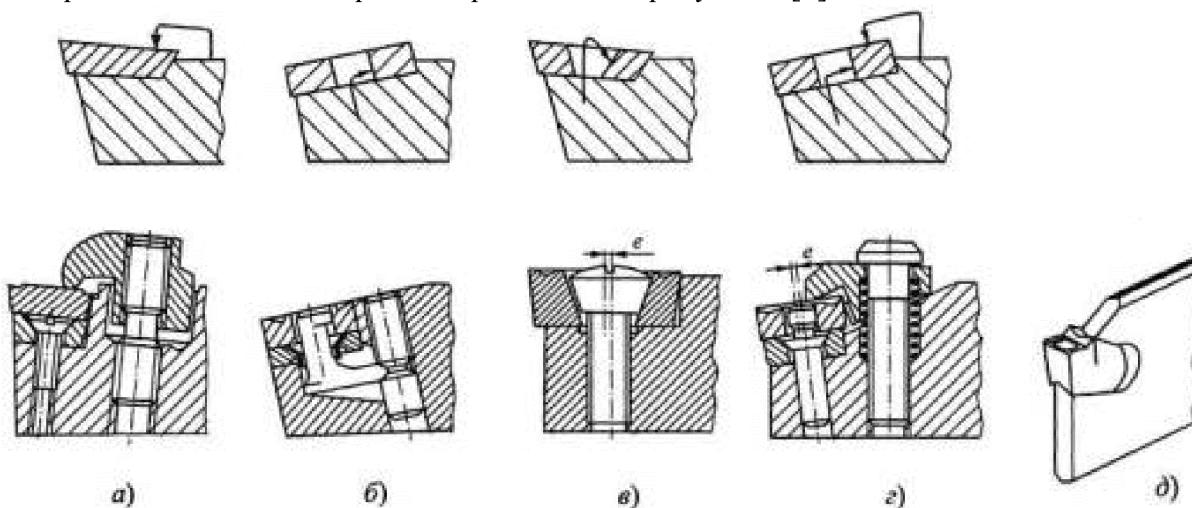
схемы механического крепления режущих пластин: а – прихватом сверху; б – рычагом через отверстие; в – винтом с конической головкой; г – штифтом через отверстие и прихватом сверху; д – за счет упругой деформации стенки паза
